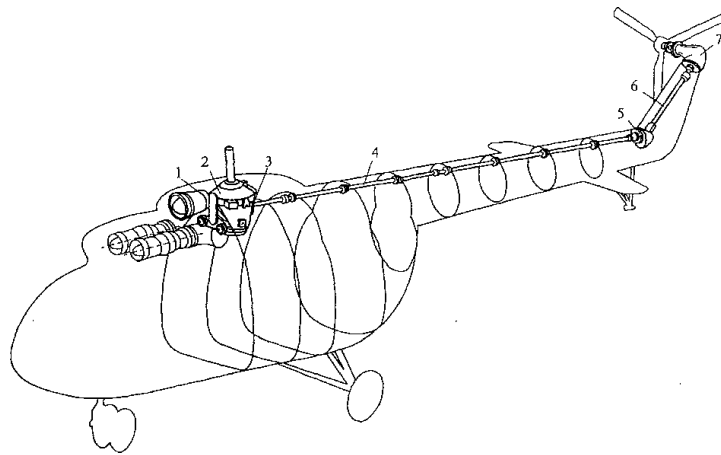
Компоновка трансмиссии вертолета [2]: 1 – промежуточные редукторы; 2 – главный редуктор; 3 – тормоз несущих винтов; 4 – вал рулевого винта; 5 – промежуточный редуктор; 6 – промежуточный вал; 7 – редуктор рулевого винта.
